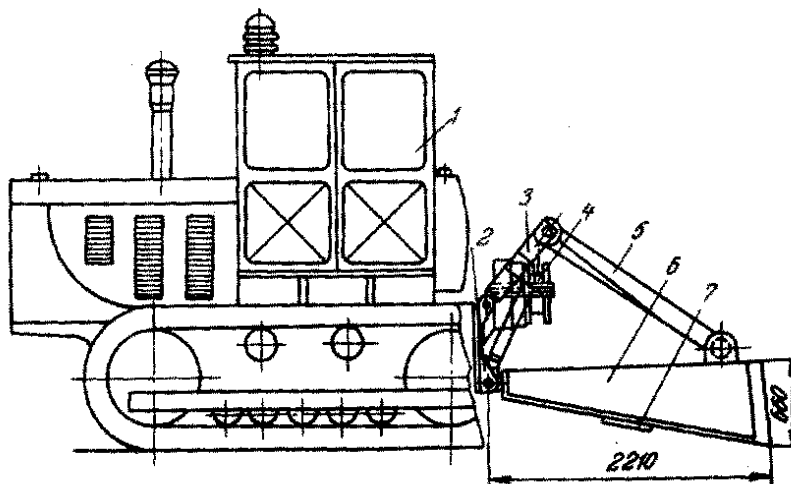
Клин-корчеватель на базе трактора Т-100:
